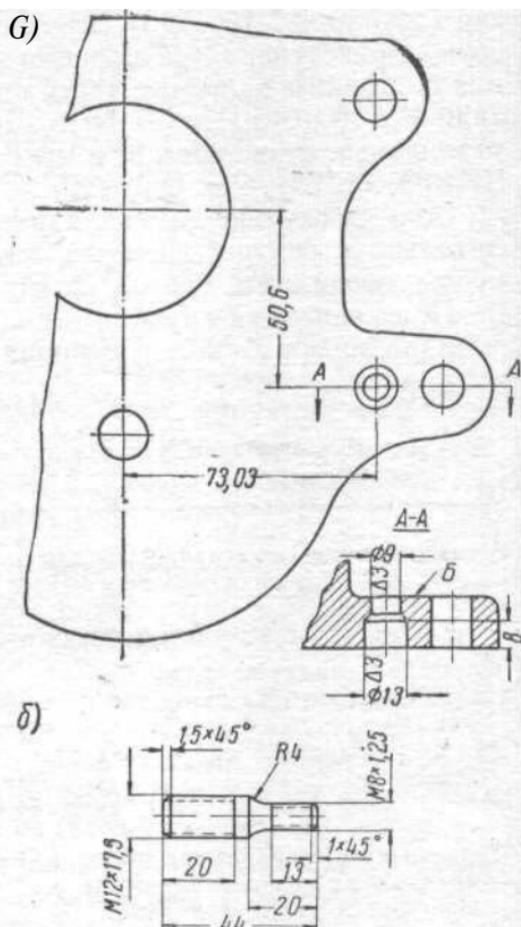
Подготовка картера коробки передач модели 407 при ее установке взамен коробки передач модели 402: а — координаты дополнительного отверстия в лапе картера; б — переходная шпилька крепления картера коробки передач к картеру сцепления
